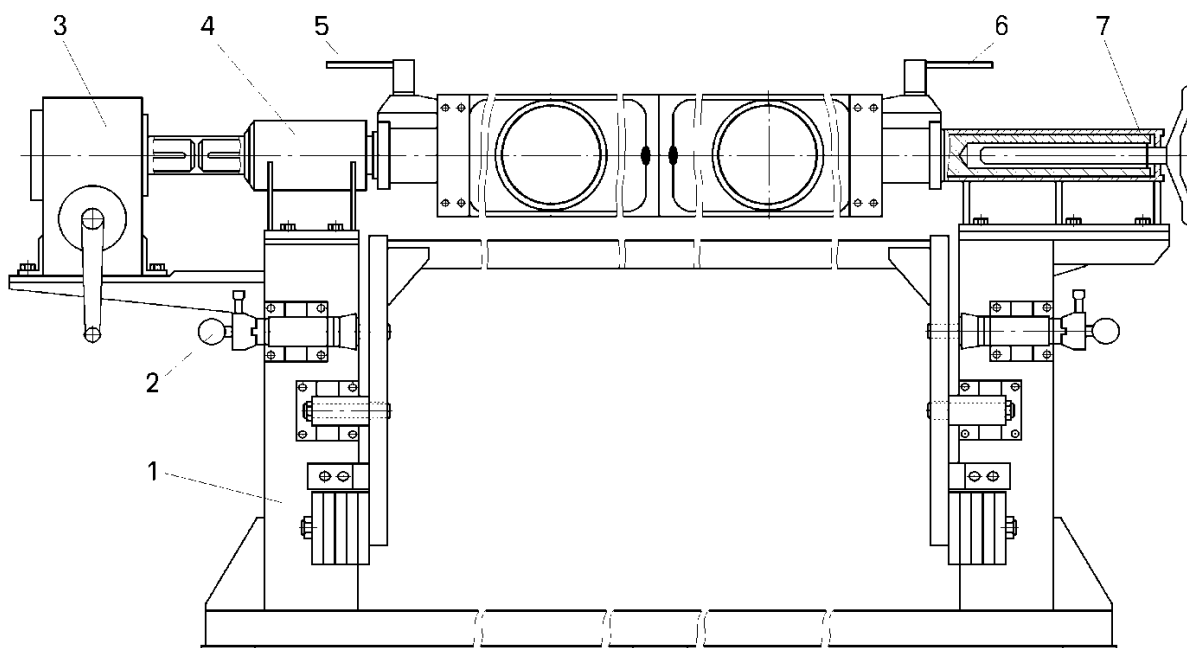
Стенд для сборки-разборки блока радиаторов:
